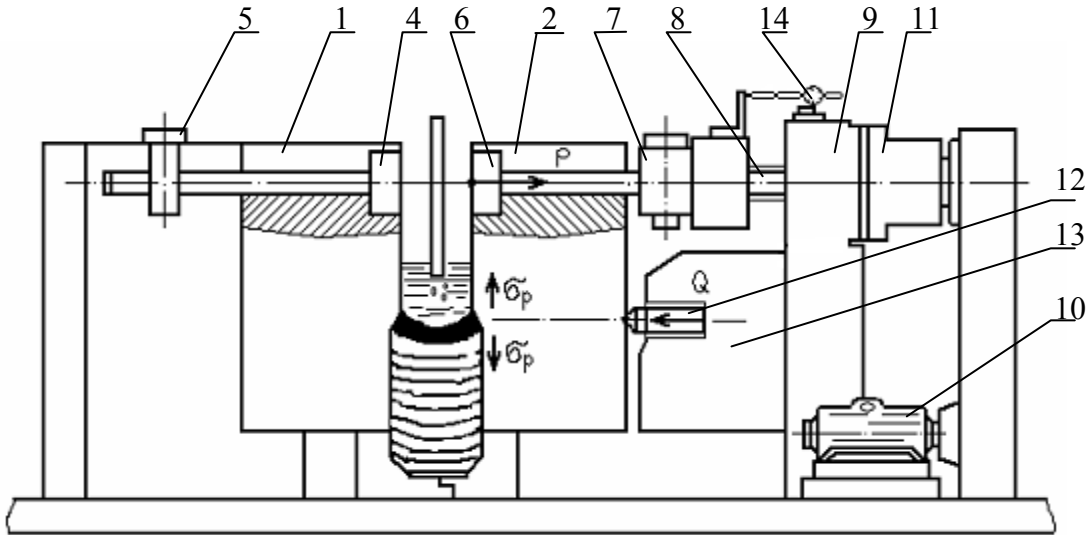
Схема установки для оценки стойкости сварного соединения против образования трещин-надрывов в условиях электрошлаковой сварки
